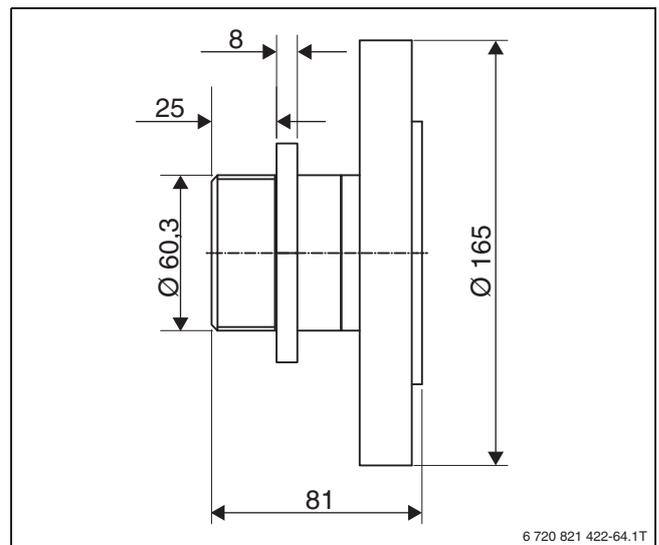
Übergangsstück für 2"-Innengewinde auf Flansch DN 50/PN 6
